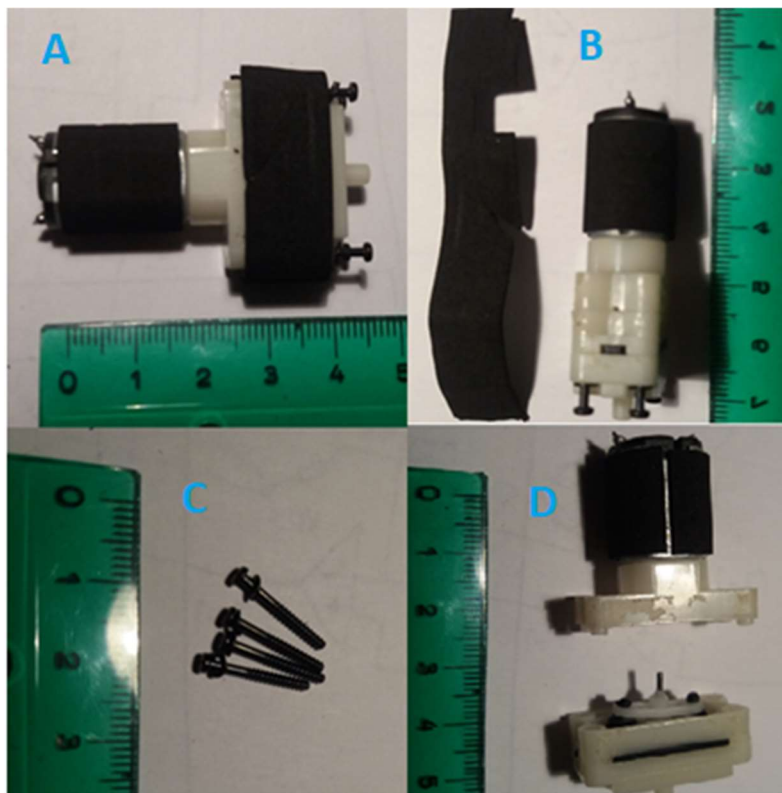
Motor (A), motor vista lateral (B), tornillos(C), separación motor de la bomba (D).
